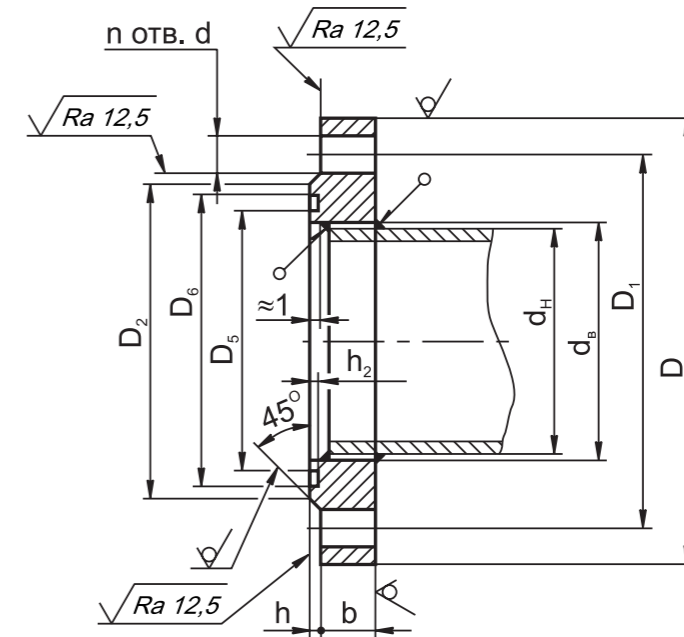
Размеры ответных фланцев для фильтров с присоединительными фланцами PN 16
